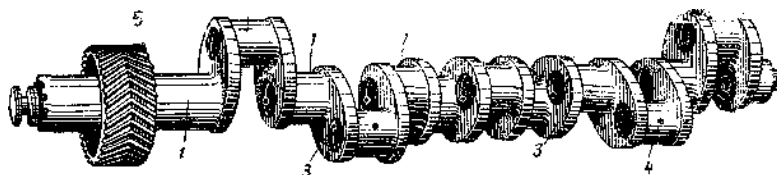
Коленчатый вал двухрядного V-образного двигателя:
